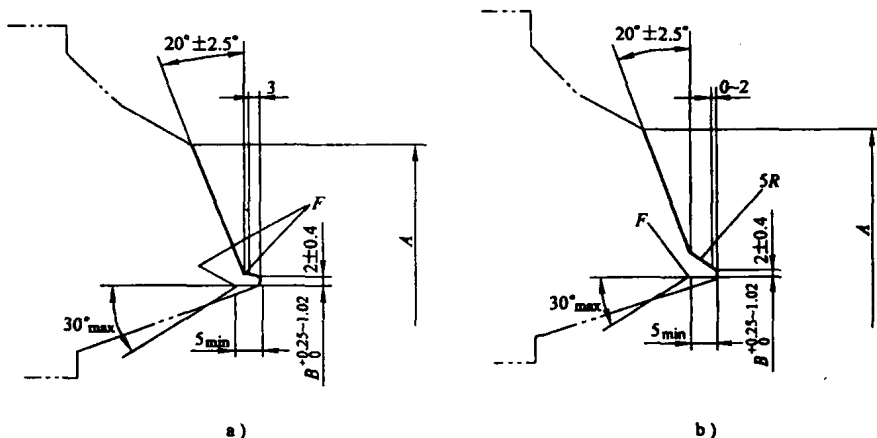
钨极弧焊根部焊道的焊接端
